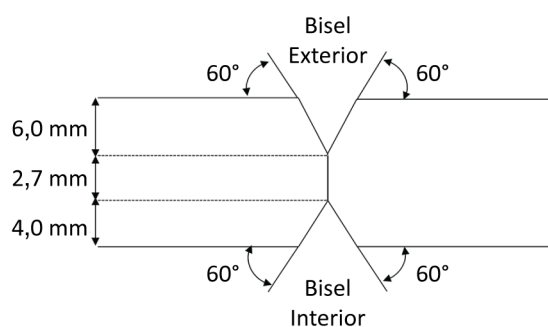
Geometría del bisel utilizado en las soldaduras.
